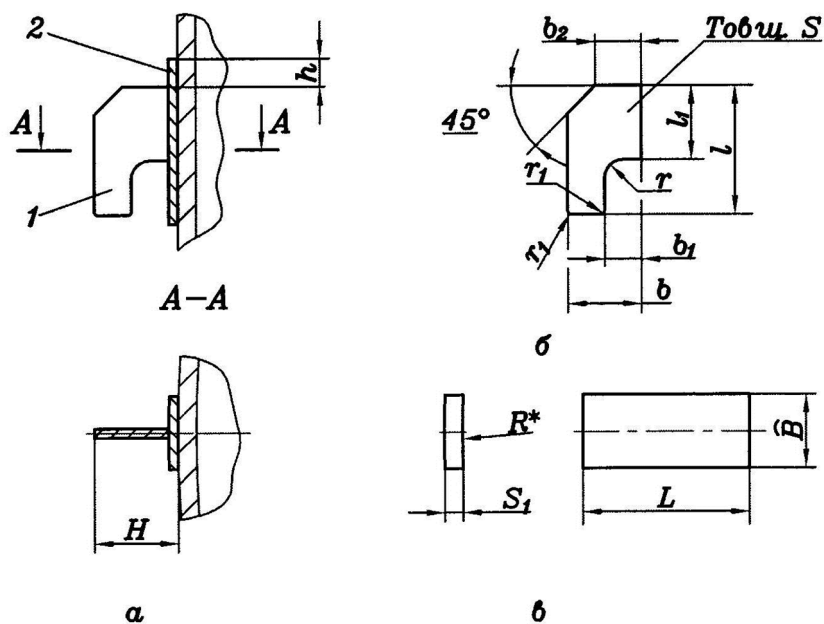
Крюк зварний (строповий пристрій типу 1 виконання 1):
